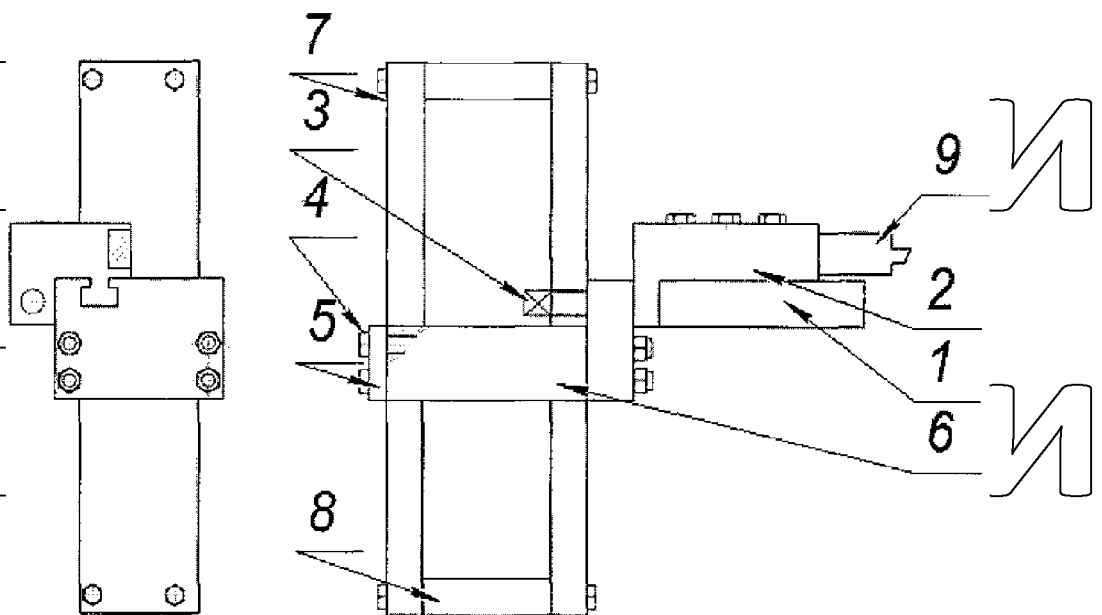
Пристрій для зачистки контактної поверхні зварювальних роликів:
